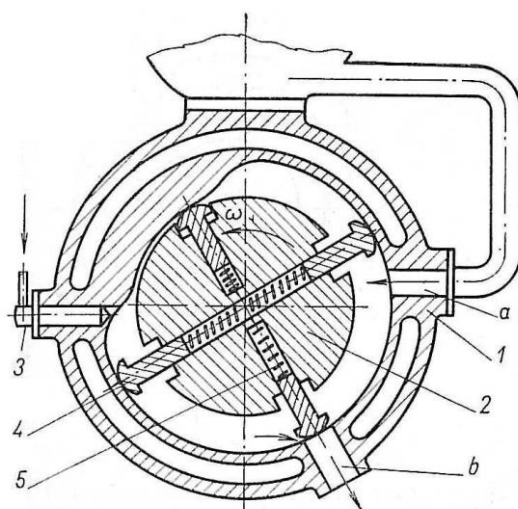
a Obr. 11-26: Motor Fillols [19]
